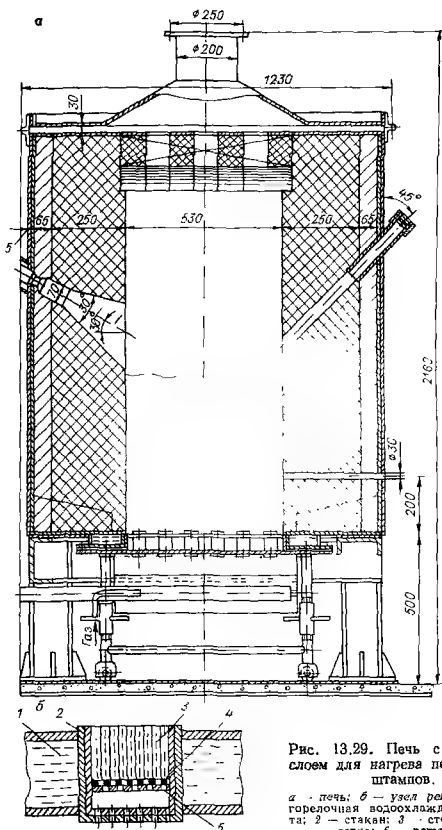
Печь с кипящим слоем для нагрева поверхности штампов.
